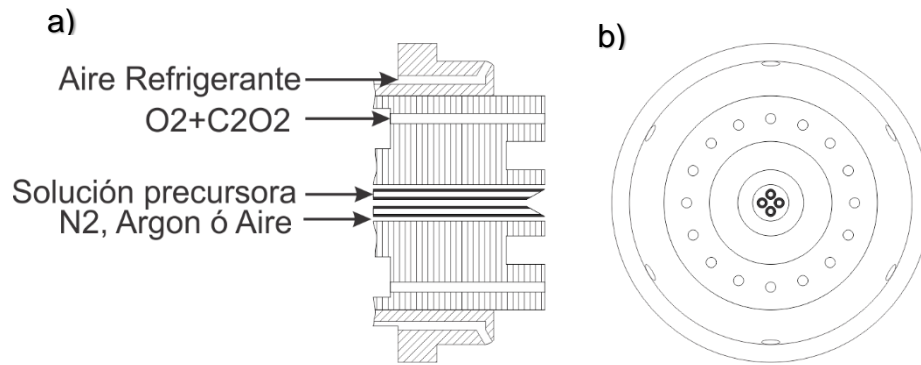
a) corte transversal de la boquilla 7 b) parte frontal de la boquilla. [22]
